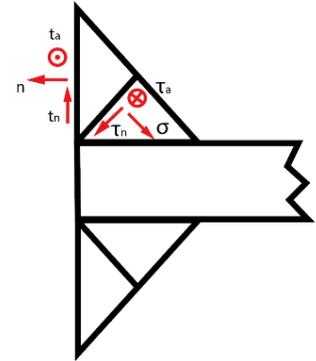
Esfuerzos internos de la soldadura
